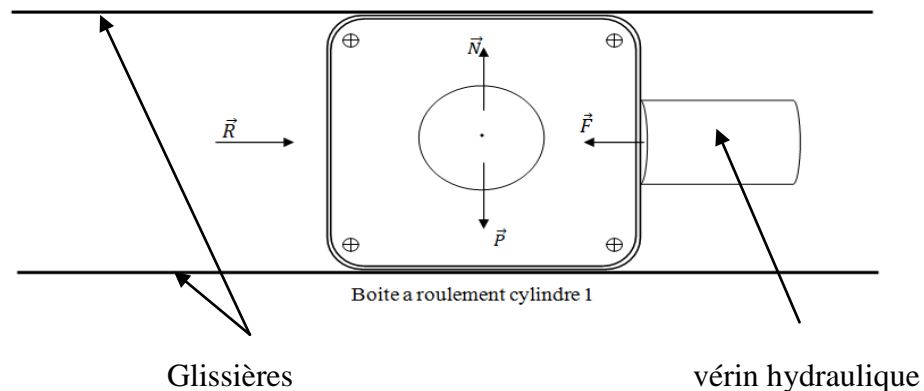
Forces appliquées sur la boîte à palier
